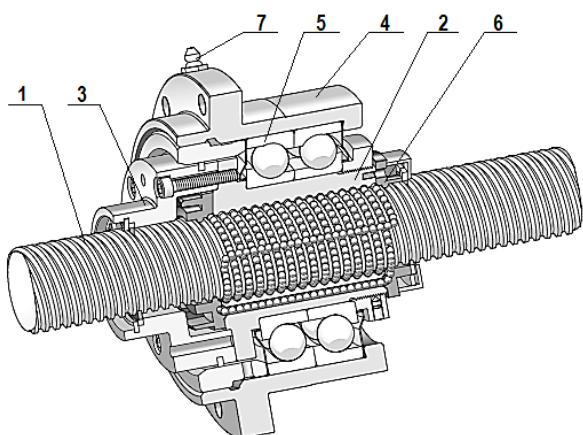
Гвинтова передача з обертовою гайкою
